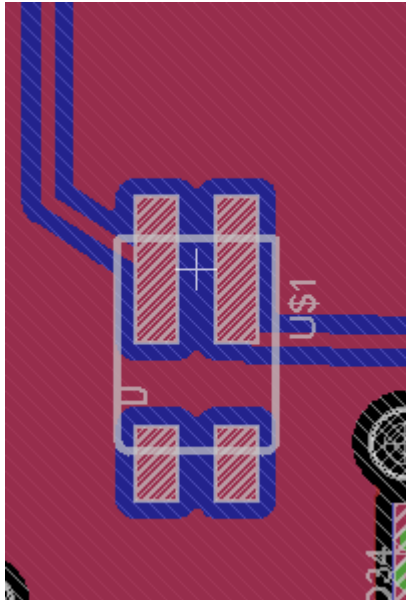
SMD Steckverbinder Board Layout und Zeichnung
